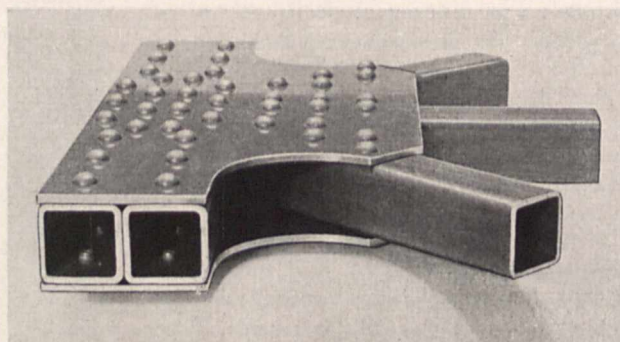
Mit Sprengnietung bearbeitetes Werkstück
